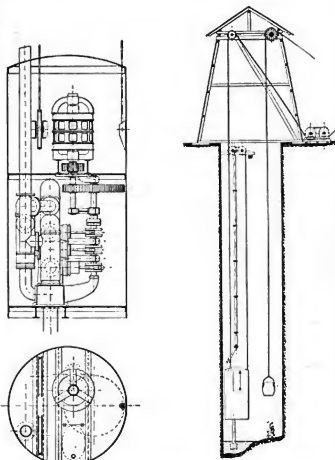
132. Drillingen-Kottenpumpe von Siemens & Halske, Berlin.
